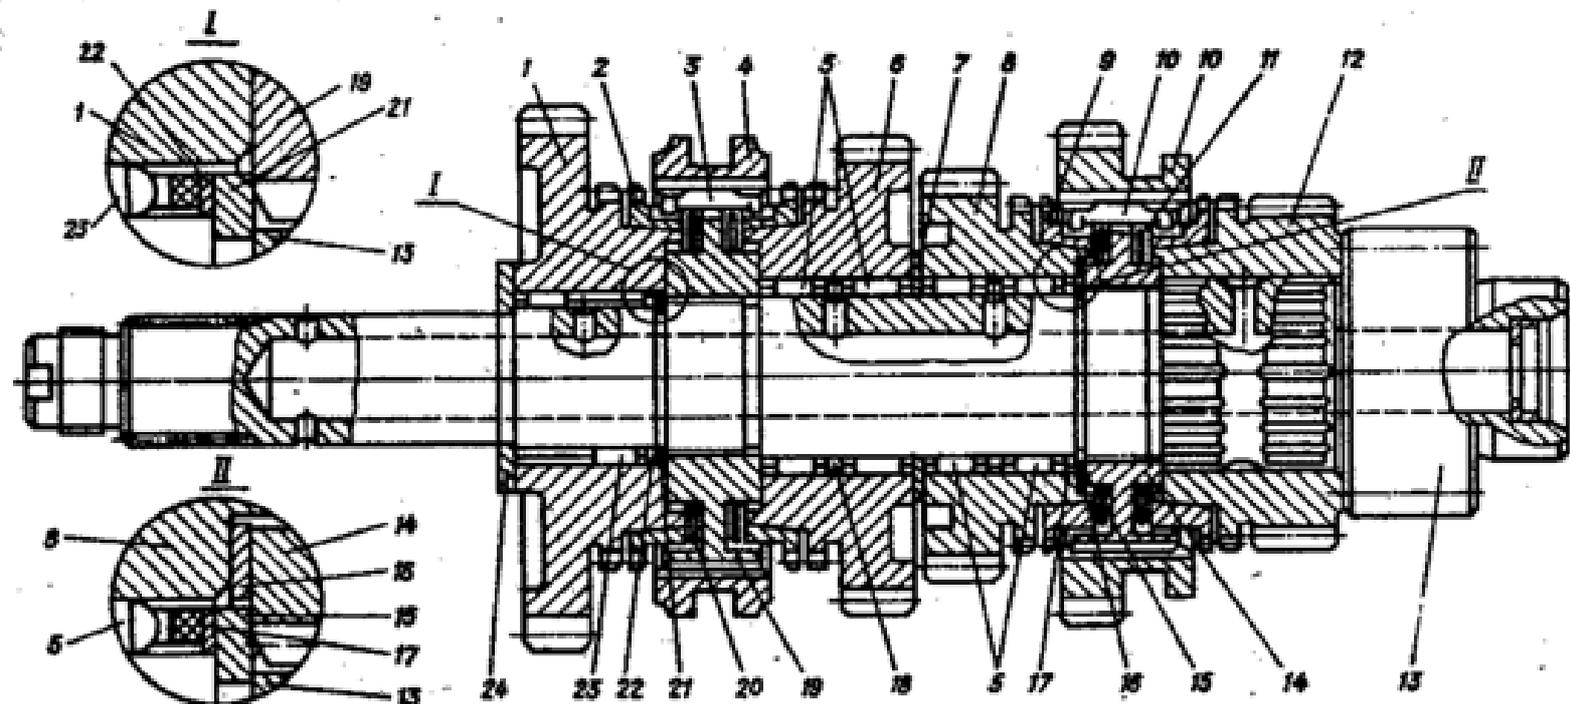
Ведущая шестерня главной передачи: 1, 6, 8 и 12 - шестерни ведомые первой, второй, третьей и четвертой передач; 2 и 9 - кольца блокирующие синхронизаторов первой-второй и третьей-четвертой передач; 3 - сухарь синхронизатора; 4 - муфта включения синхронизатора первой и второй передач; 5 - подшипники ведомых шестерен второй-третьей передач; 7, 16 - шайбы упорные; 10 - шестерня ведомая заднего хода; 11 и 20 - пружины синхронизатора третьей-четвертой и первой-второй передач; 13 - шестерня ведущая главной передачи; 14 и 19 - ступицы муфт переключения третьей-четвертой и первой-второй передач; 15, 21 - кольца стопорные; 17, 22 - кольца; 18 - проставочное кольцо; 23 - подшипник ведомой шестерни первой передачи; 24 - шайба упорная
